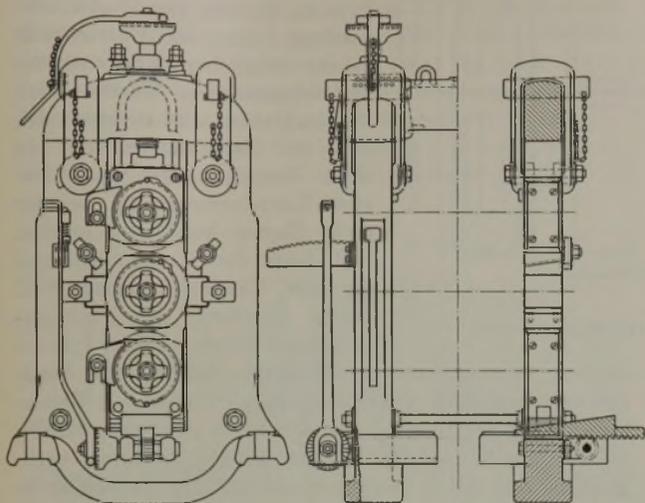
Rollenlagereinbau für Trio-Walzengerüst.
